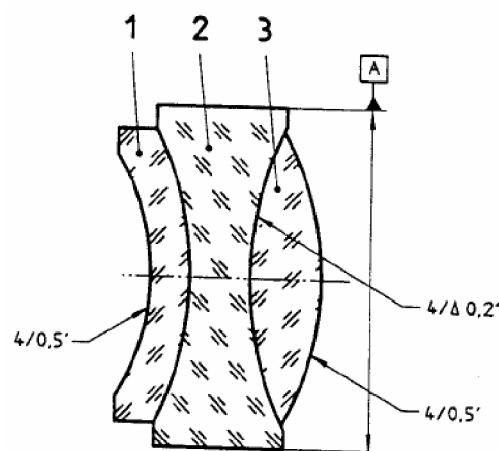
Складальний вузол, включаючий позначення допуску на клейовий клин; базова вісь, визначається зовнішнім циліндром
